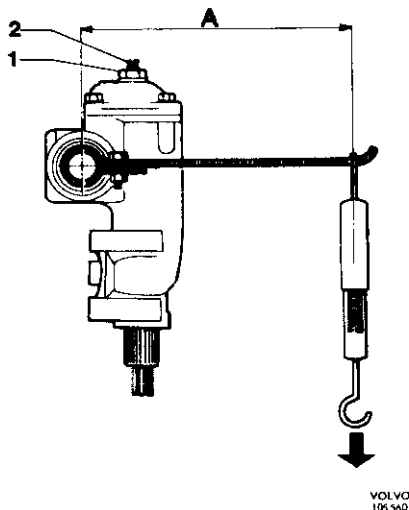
Kontrolle des Flankenspiels: Lenkschnecke-Lenkrolle
